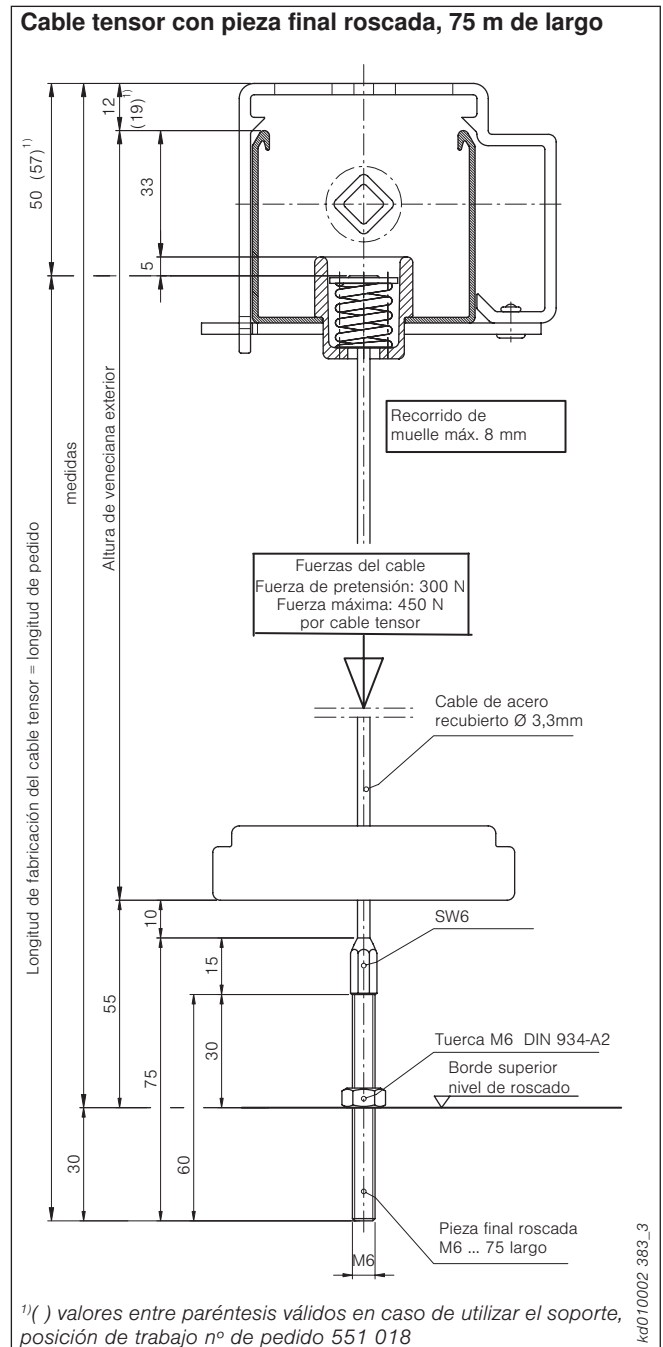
Cable tensor con pieza final roscada, 75 mm de largo
